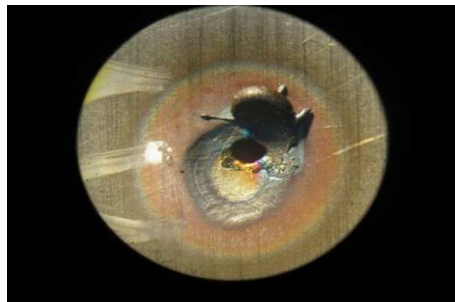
10. Punto de soldadura en la probeta de 2 mm a 5x.
